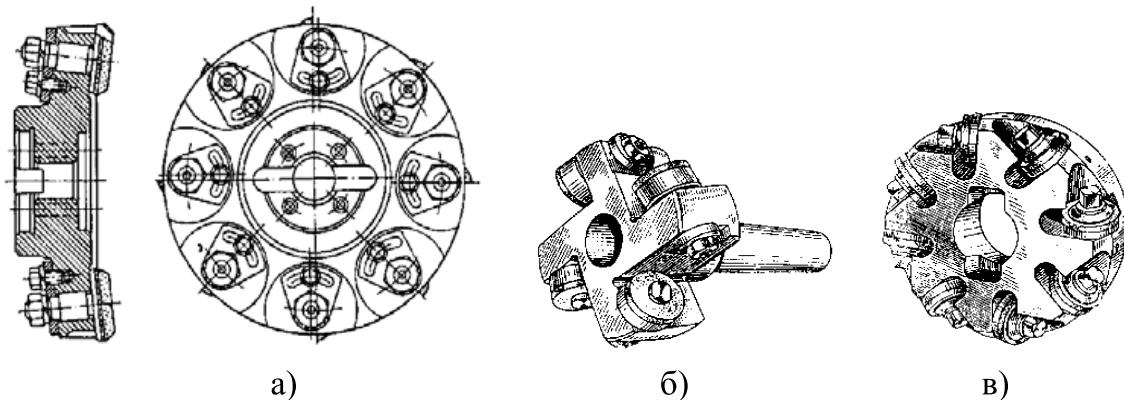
Фреза торцева із твердосплавними кільцями (а - конструкції Л.В. Ємельянова і К.І. Сокольського; б - Є.А. Белова; в - В.Д. Сердюка)
